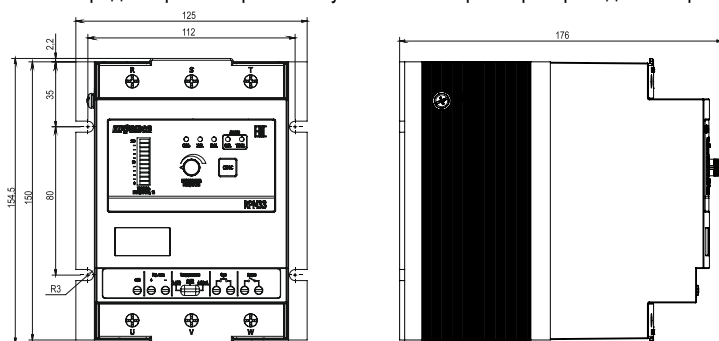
Габаритные размеры RPM33-25.VAR
